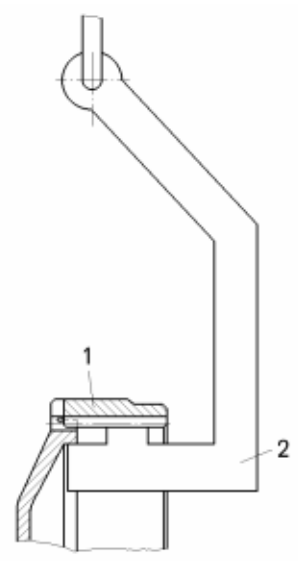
Приспособление для снятия и установки коронной шестерни со ступицей колесной передачи:
